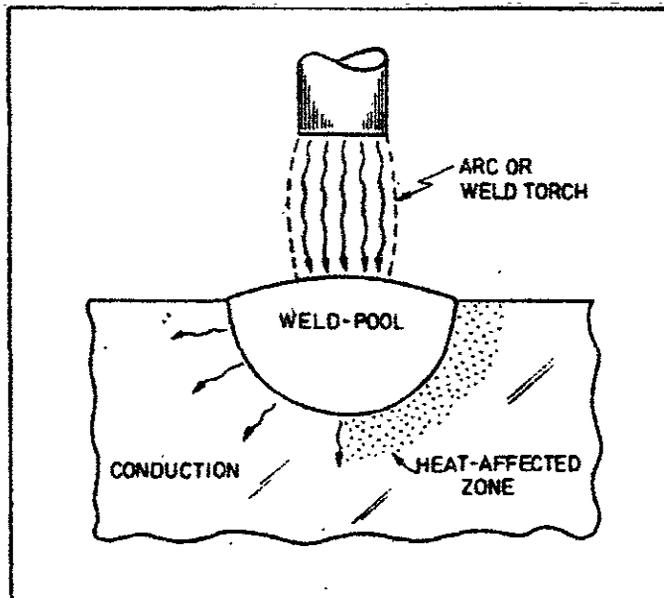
Soldadura. Una antorcha funde ambas piezas a trabajar, agregando soldadura de metal la cual al ser depositada es cubierta por una pequeña cascara. (Tomada de la referencia [1]).
